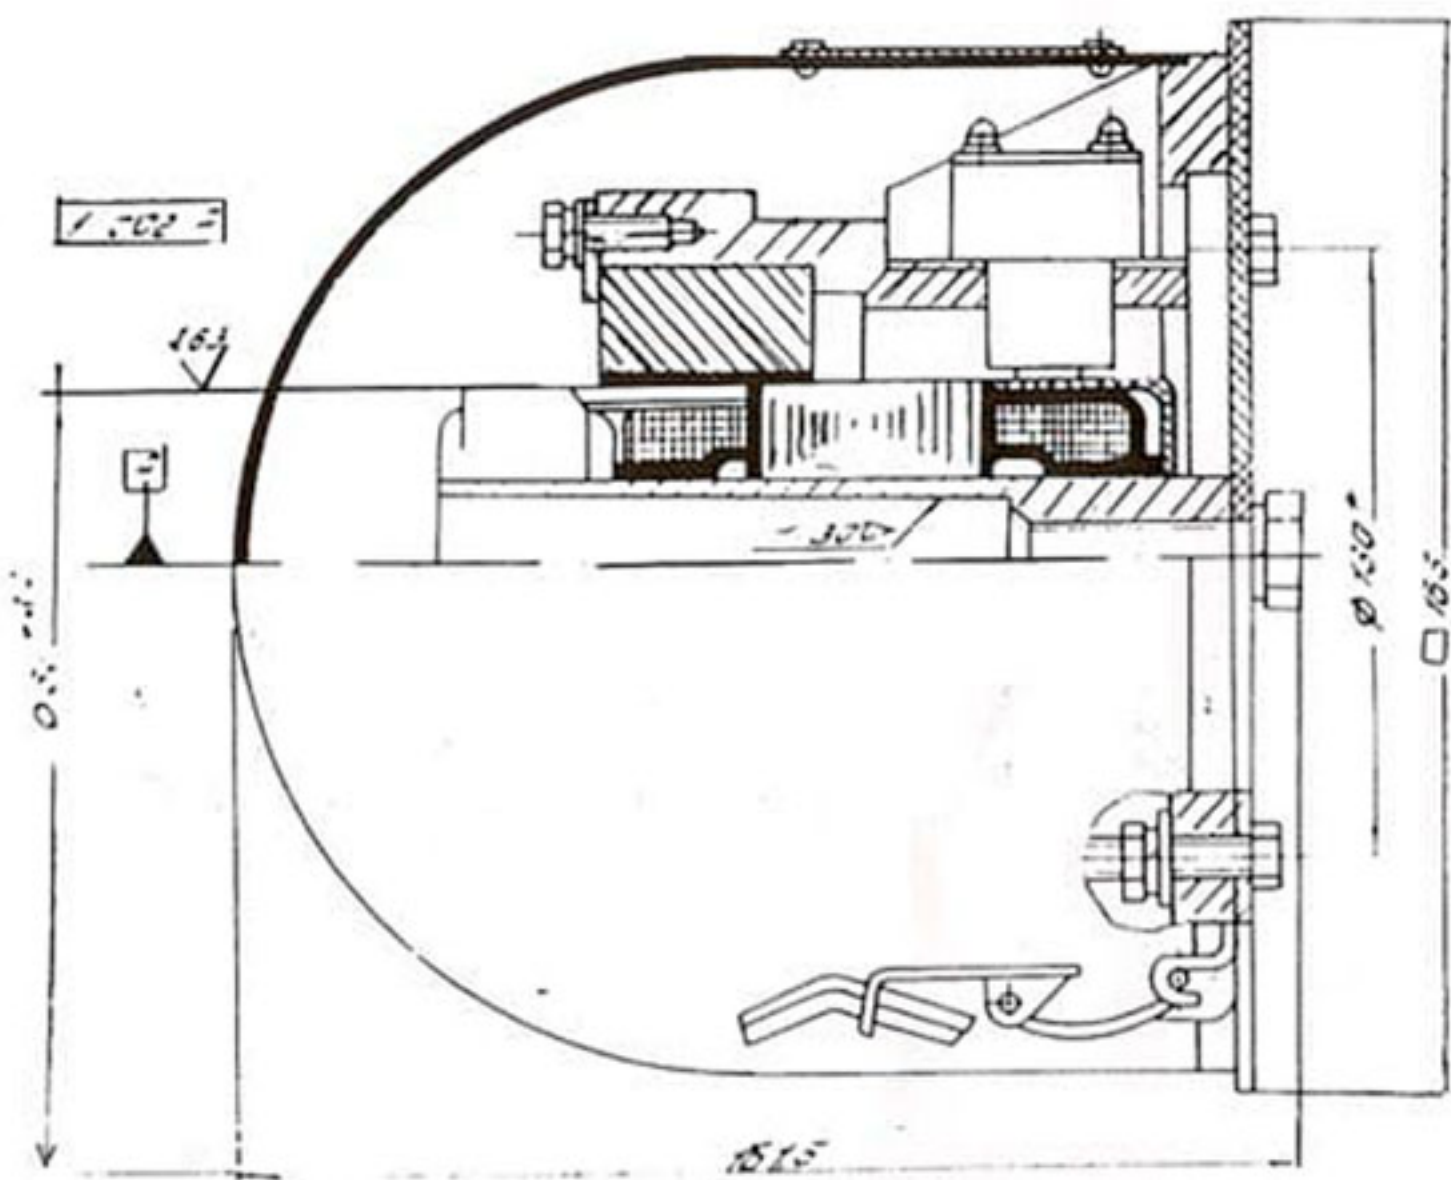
Габаритные, установочные и присоединительные размеры.
